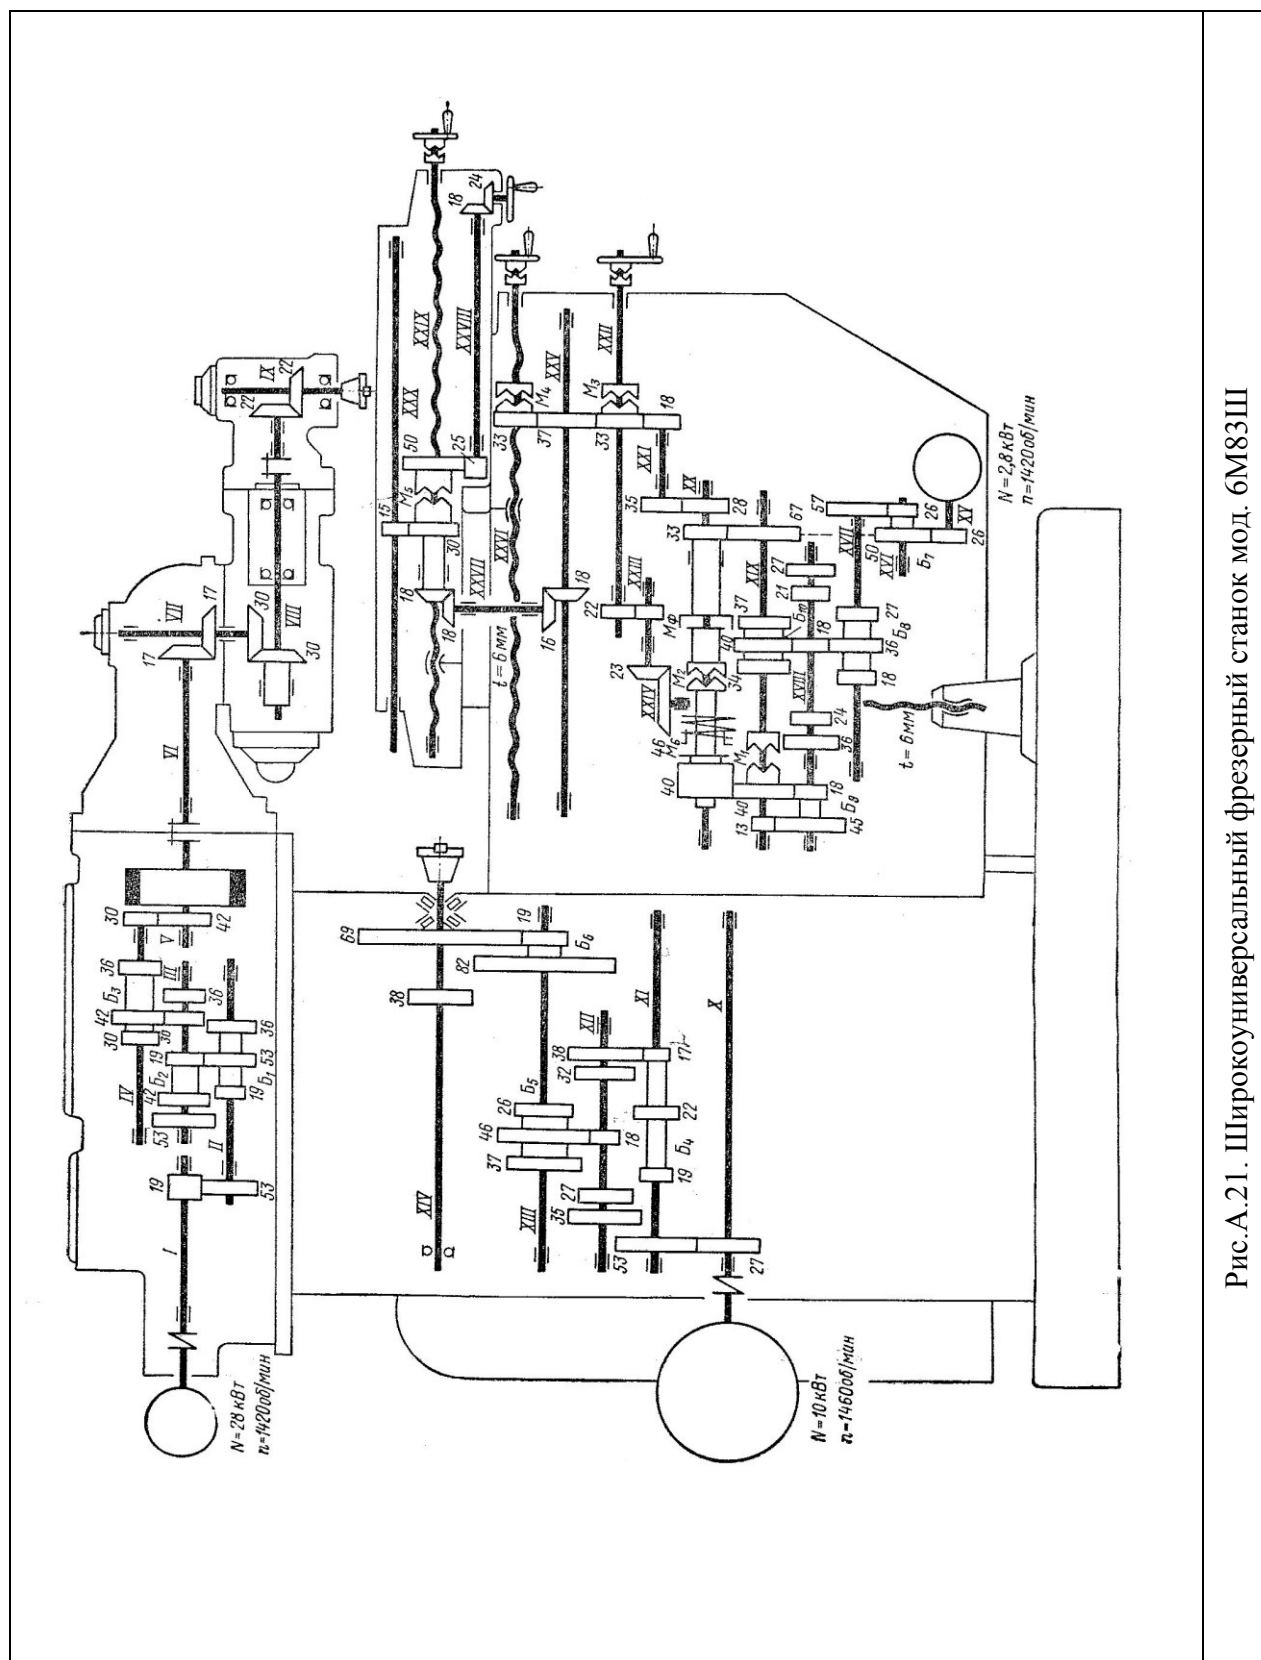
Широкоуниверсальный фрезерный станок мод. 6М83Ш
